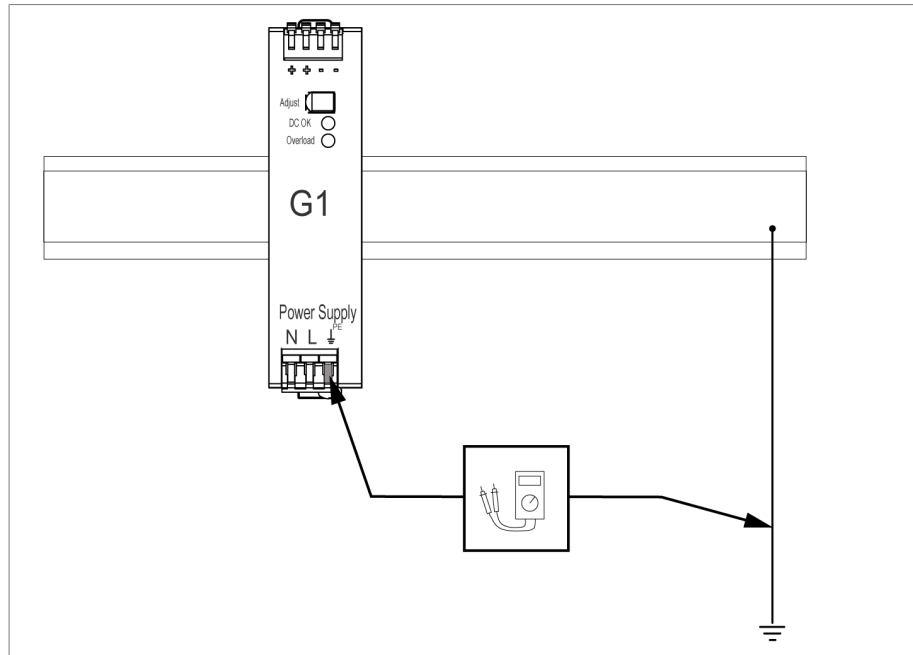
Проверка заземления модуля G1 PULS DIMENSION QS3.241
